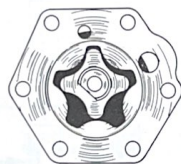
Vista frontal de la bomba de aceite sin tapa.
